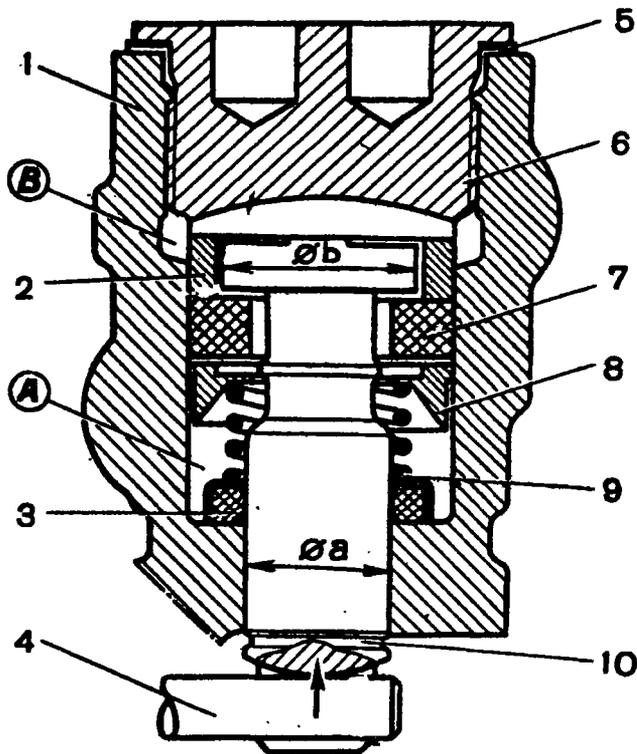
Регулятор давления задних тормозов в нерабочем положении: А - полость нормального давления; В - полость регулируемого давления; Р - усилие, передаваемое рычагом 4 привода регулятора; 1 - корпус регулятора; 2 - распорная втулка; 3 - уплотнительное кольцо; 4 - рычаг привода регулятора; 5 - пробка; 7 - резиновый уплотнитель; 8 - тарелка пружины; 9 - пружина поршня; 10 - поршень
